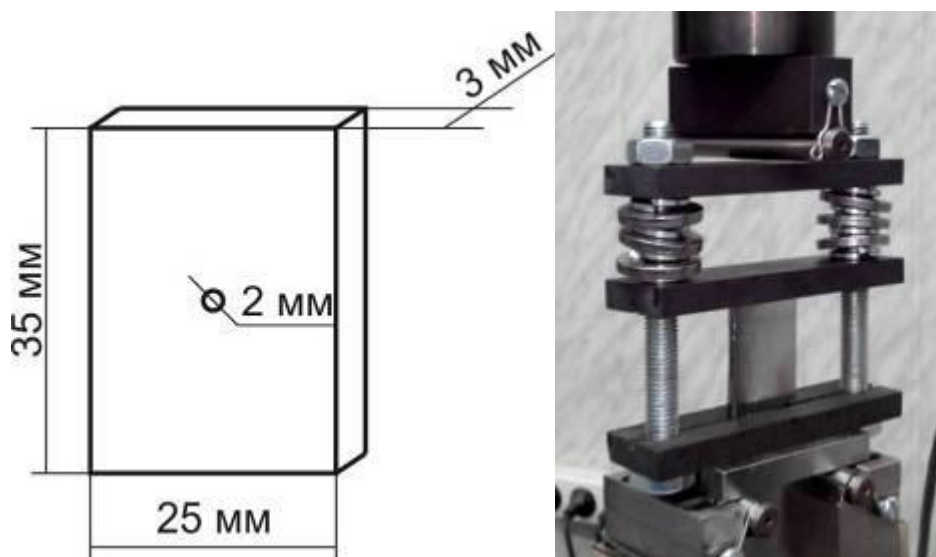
Схема образца и внешний вид приспособления для создания в материале сжимающих напряжений
